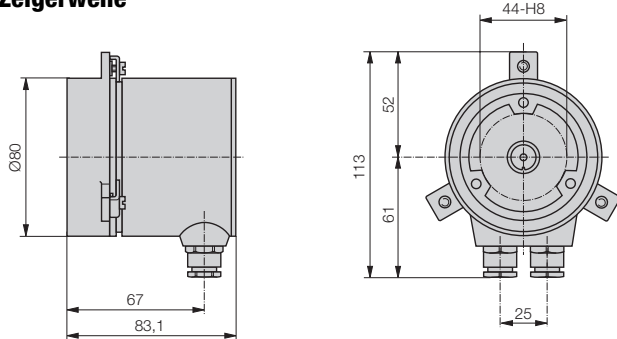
Grundgerät zum Anbau an Messgeräte mit drehbarer Zeigerwelle.
